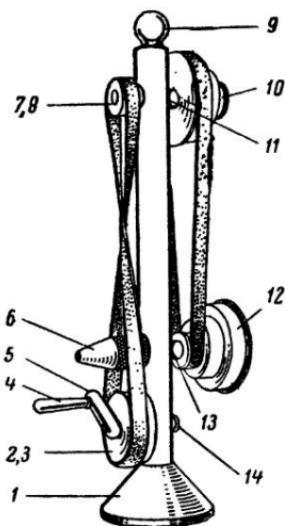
Модель плоско-ременной передачи со шкивами: 1 — основание; 2 — ведущий шкив привода; 3 — стопорный винт; 4 — ручка; 5 — рычаг привода; 6 — гайка; 7 — ведомый шкив привода; 8 — стопорный винт; 9 — стойка; 10 — ведущий шкив рабочего вала; 11 — ведущий вал передачи; 12 — ведомый шкив рабочего вала; 13 — рабочий вал («шпиндель»); 14 — ведущий вал.
